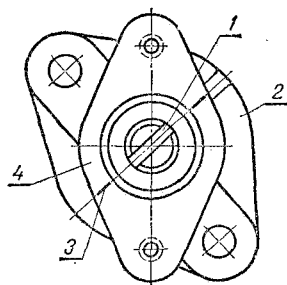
Схема установки привода прерывателя-распределителя Р4-В:
